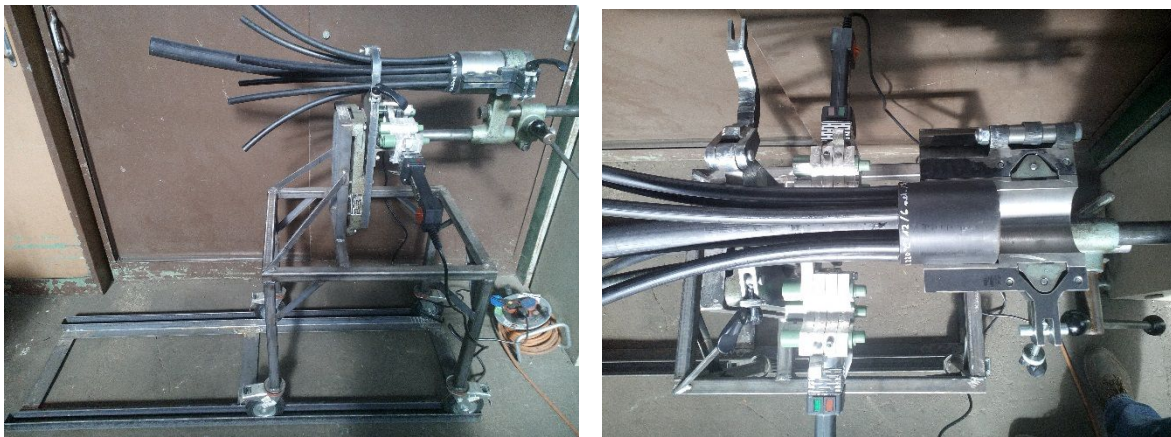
Schweißvorrichtung (erste Version); rechts: Detailaufnahme
